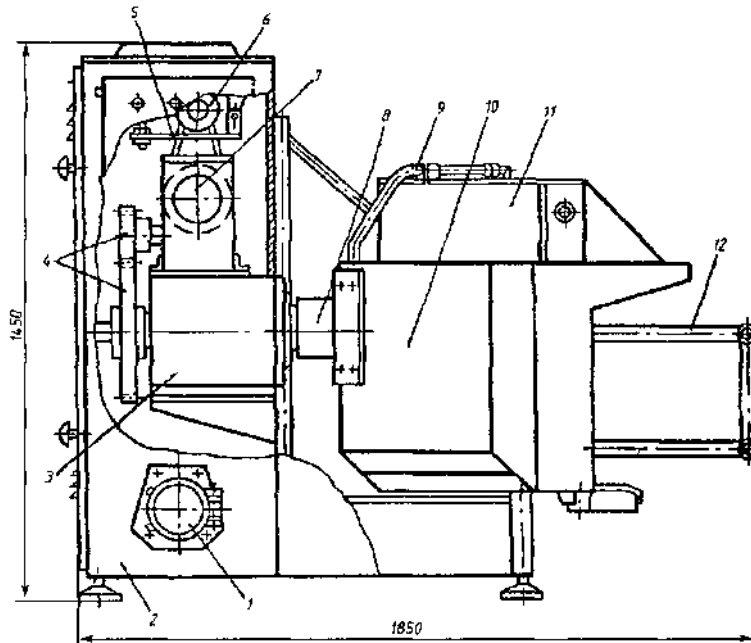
Установка для тумблерування м'яса Я2-ФММ: 1 – пастка-розширювач; 2 – станина; 3 – підшипникова опора; 4 – зубчаста передача; 5 – клинопасова передача; 6 – електродвигун; 7 – черв'ячний редуктор; 8 – вал корпусу; 9 – вакуумпровід; 10 – корпус; 11 – кришка; 12 – напрямні
